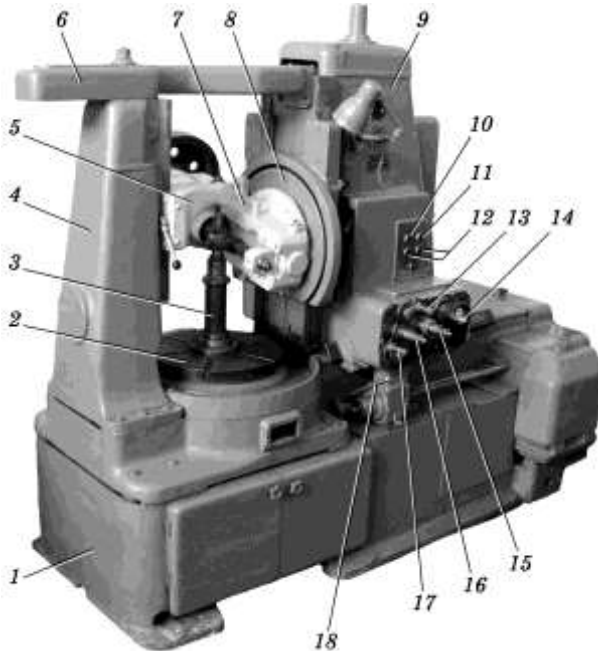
Зубцефрезерний напівавтомат 5Д32
